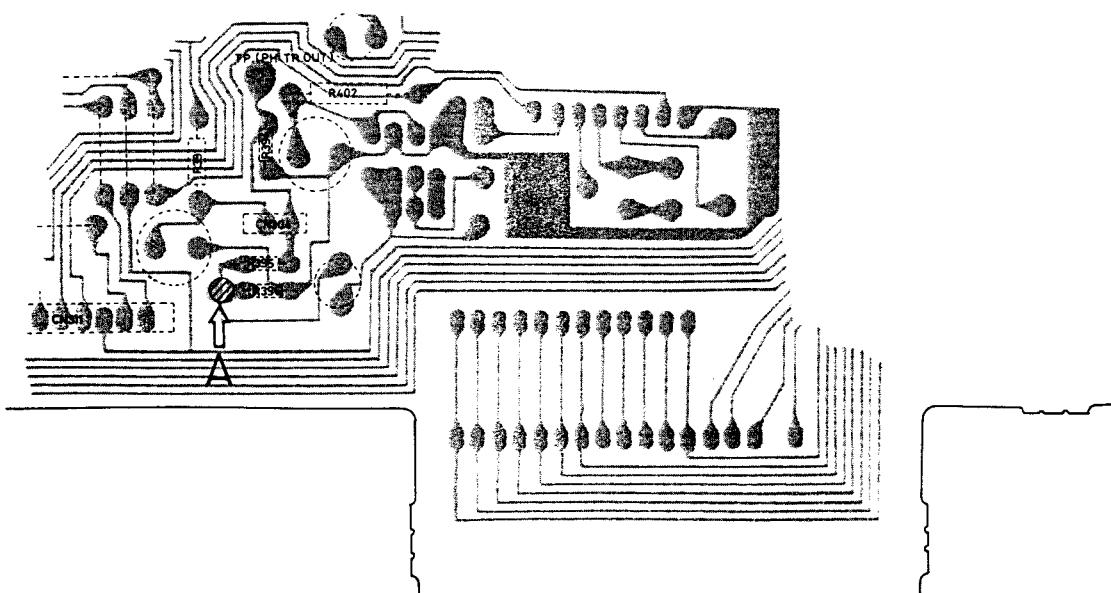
Lugares de ajuste (en el lado de chapa del conjunto principal)
